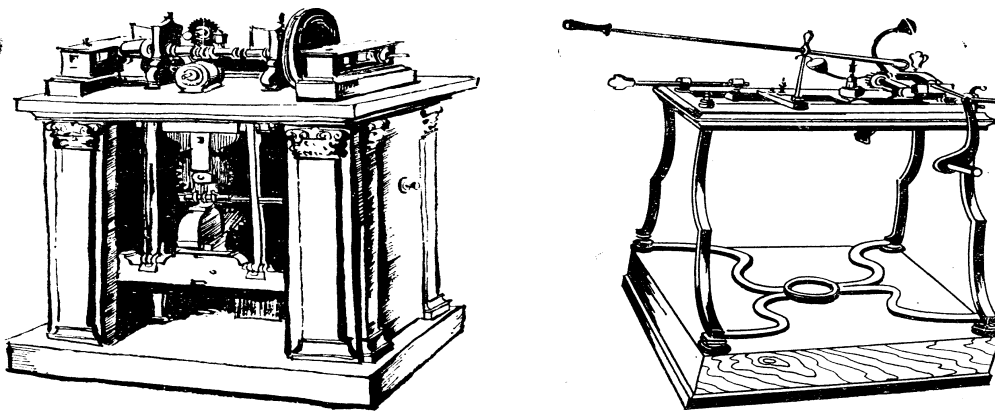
Токарно-копіювальний верстат і зубофрезерний верстат
